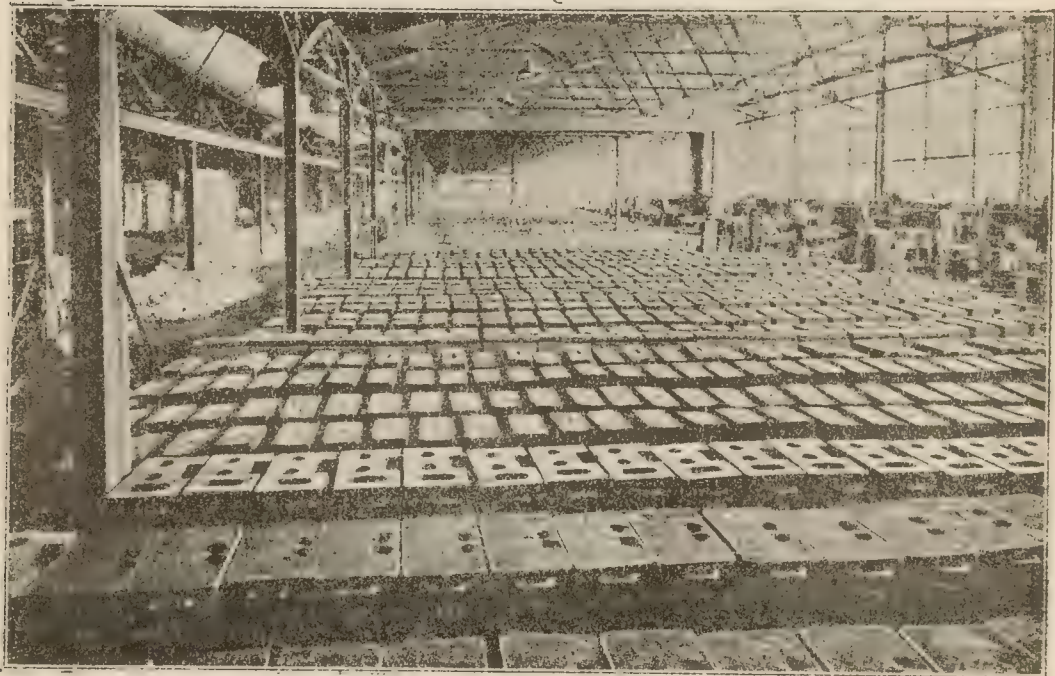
Камера для очистки отливок пескоструйным аппаратом.
